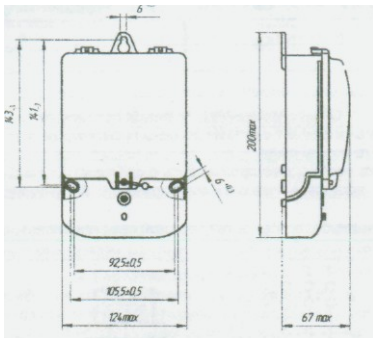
Общий вид счетчика в корпусе типа Ш1
